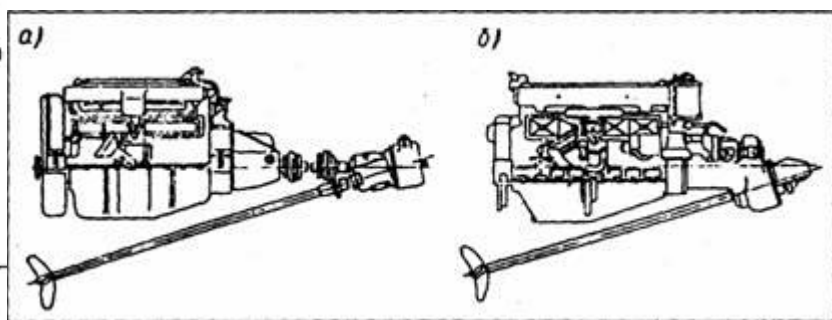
Два вида углового редуктора для стационарного двигателя:
